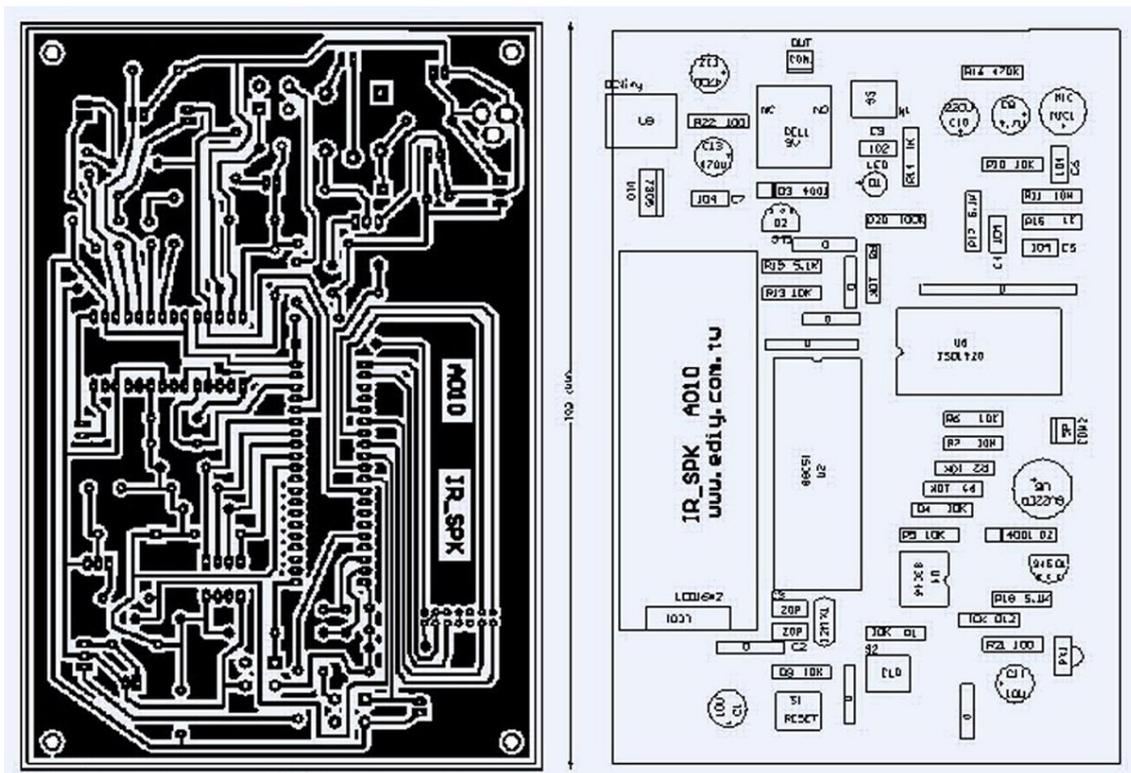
電子密碼鎖之電路板 Layout 圖
